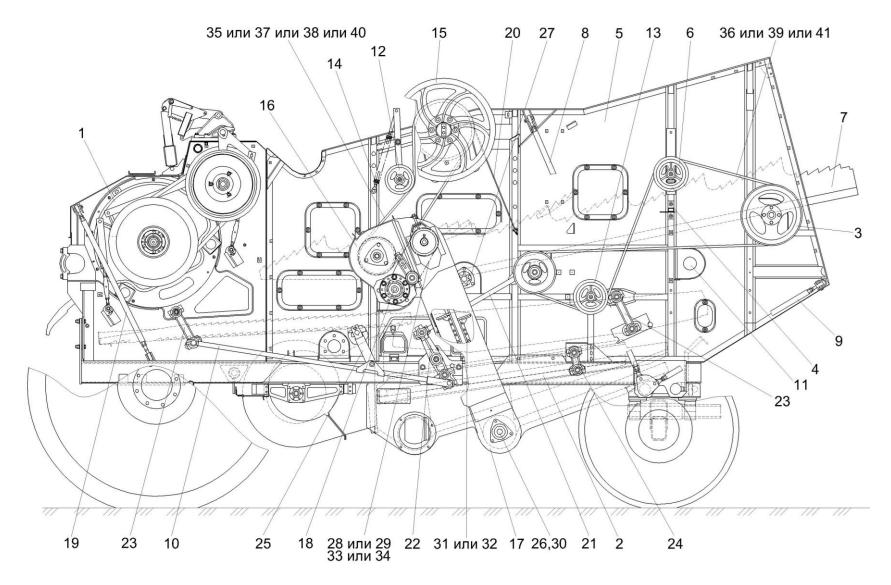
Очистка КВК-8А-0202000-02 (вид слева)
